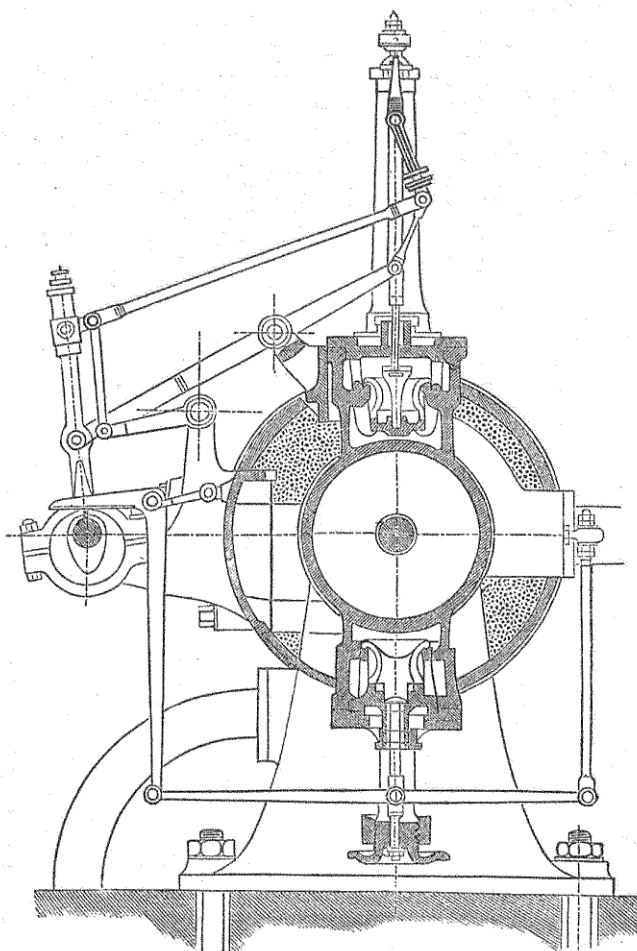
Coupe d'une machine Sulzer à soupapes.
